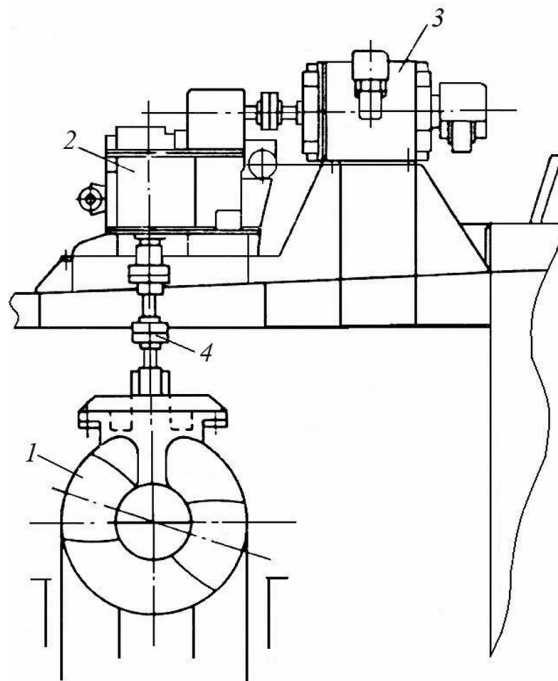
ПП з реверс-редуктором: 1 – гребний гвинт; 2 – реверс-редуктор із гідравлічними муфтами; 3 – електродвигун; 4 – вертикальний валопровід
